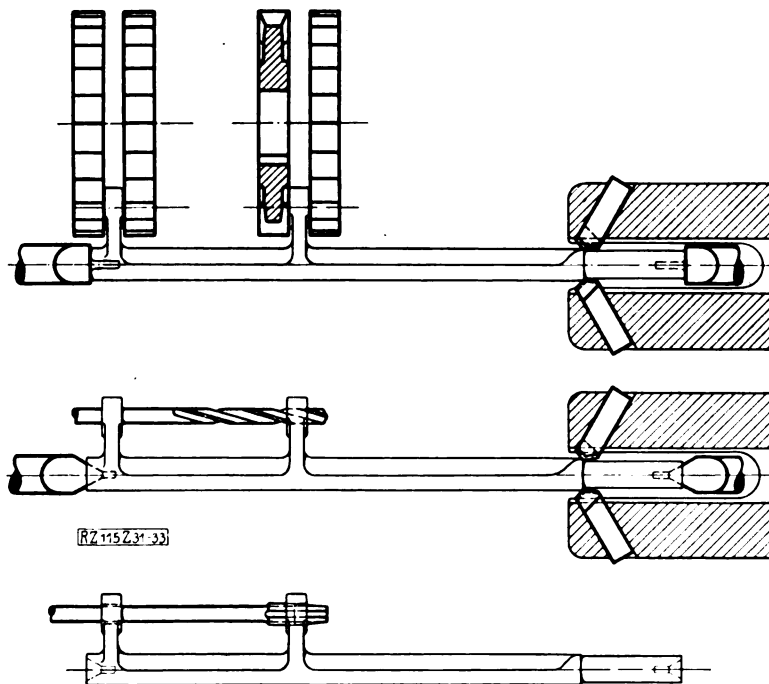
bis 33. Bearbeitung von Hebe- und Schiebewellen, Abb. 30, auf Sondermaschine, Abb. 29 (Textbl. 1).
